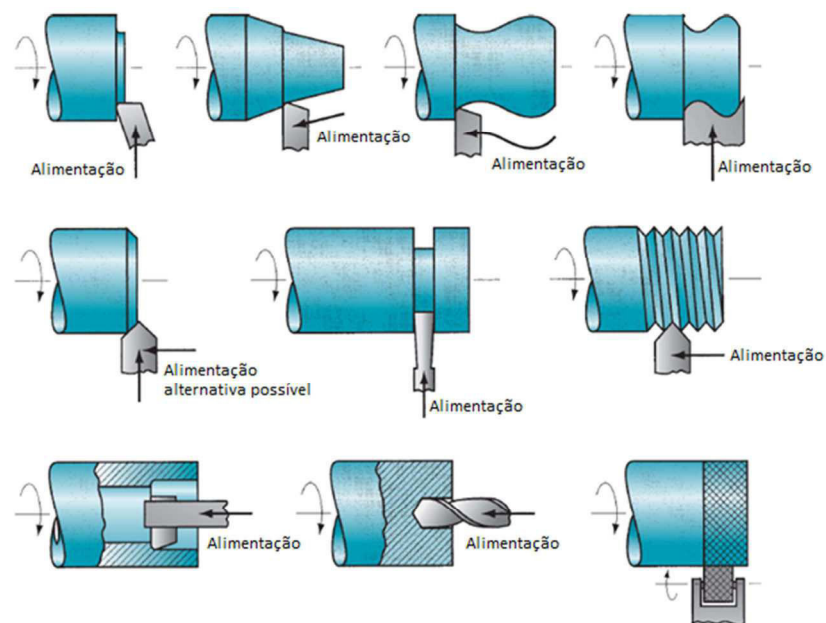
Métodos de torneamento [FONTE: adaptado [58]].
